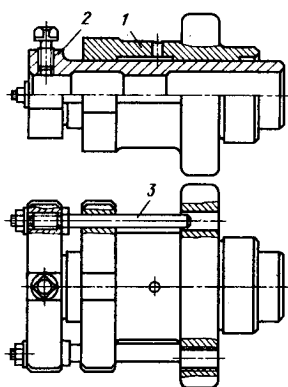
Приспособление для крепления резьбонарезных головок: 1 — корпус; 2 — пиноль для крепления резьбонарезных головок; 3 — скалка
